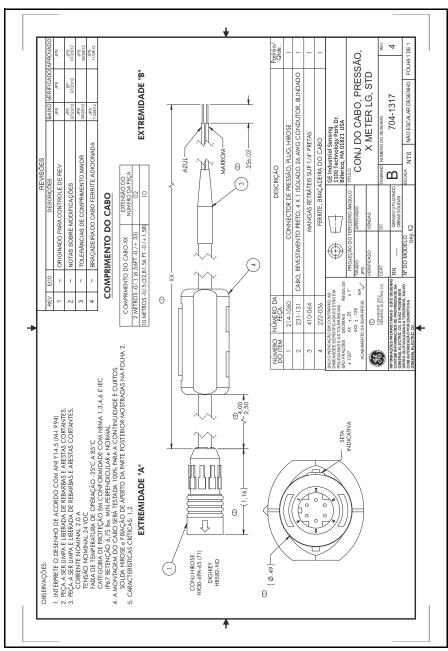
Cabo, Padrão (ref. des. 704-1317, FL 1 de 2)
